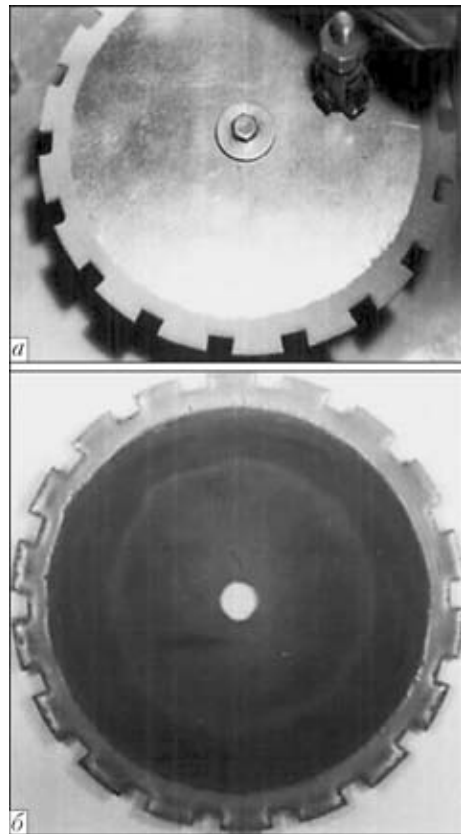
Устройство для засыпки шихты (а) и наплавленный диск (б) [34]
